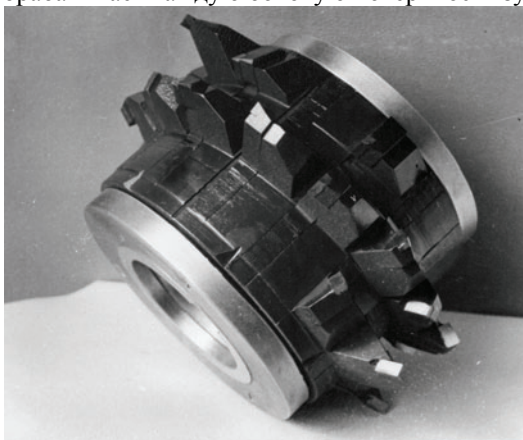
Схема фрезы с настроечным перемещением зубчатых реек.
